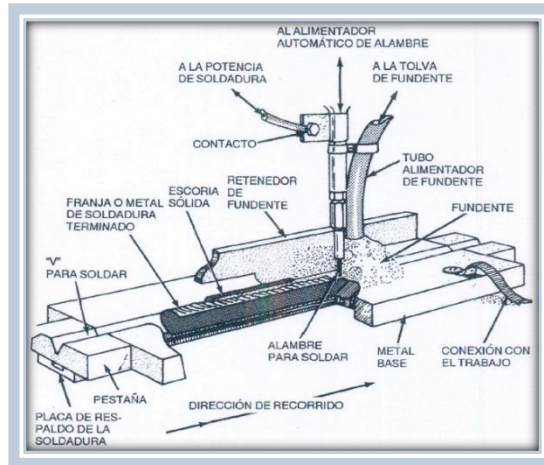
Esquema del proceso de soldadura por arco sumergido [3]
